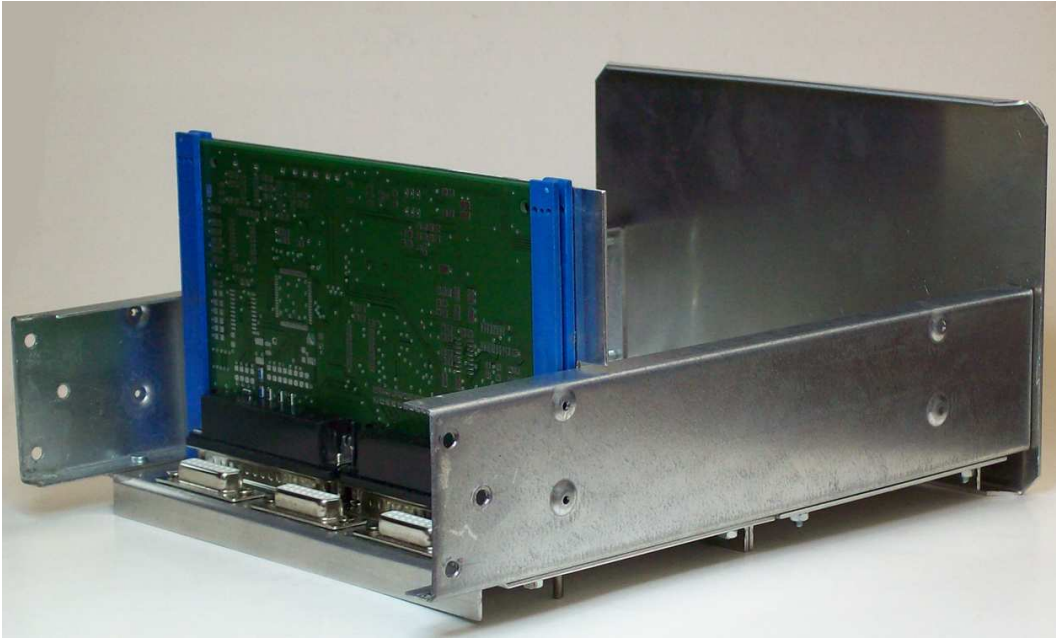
Gehäuseaufbau seitlich mit unbestücktem Steuerrechner
